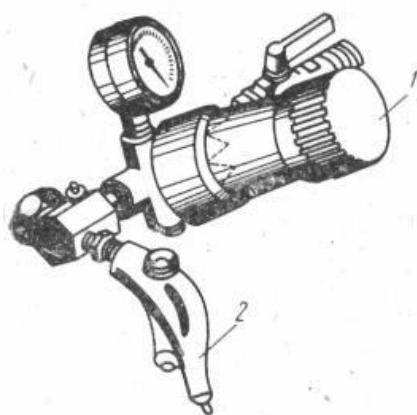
Regulator de aer comprimat cu injectorul de aer :
